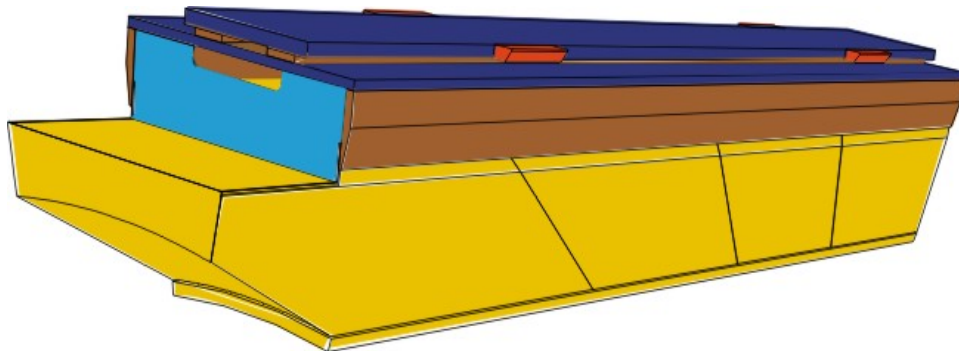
Vue tri-dimensionnelle d'un supermodule.
